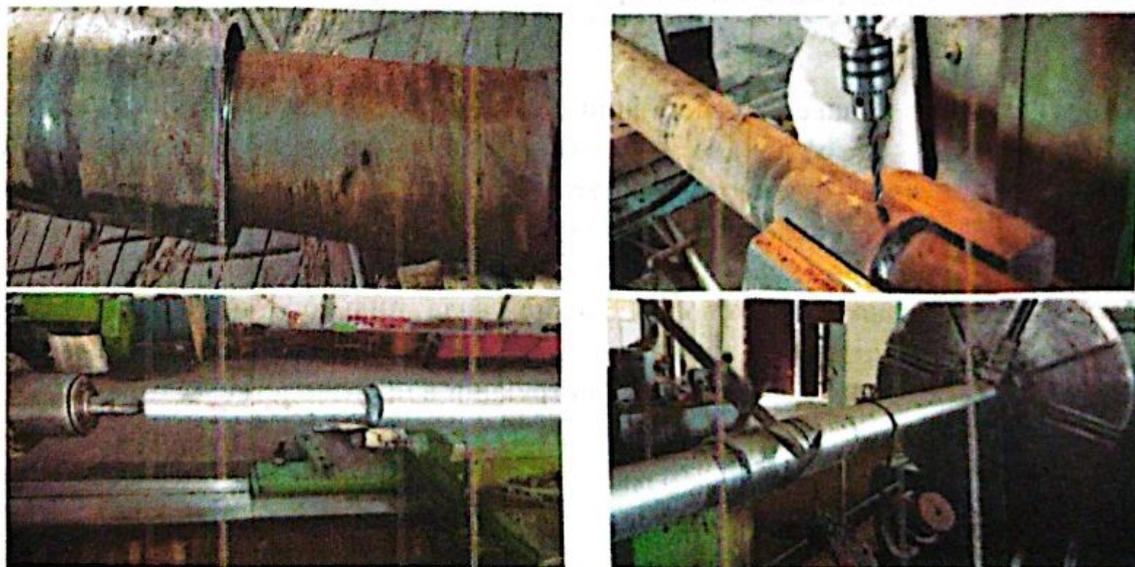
Процесс изготовления пилотного экземпляра рекомендуемой конструкции вала
